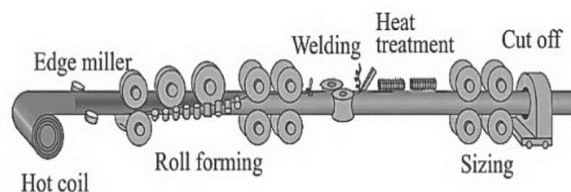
Processo de soldadura longitudinal de tubo [16]
